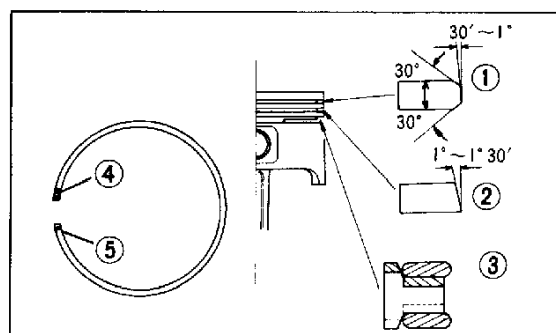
(1) Oberster Kolbenring (4) Firmenbezeichnung
